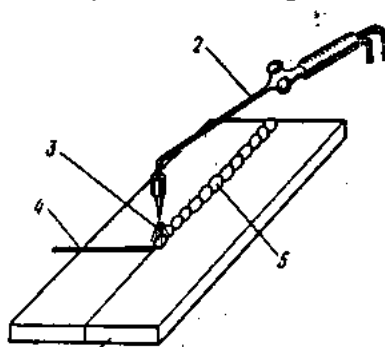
Газовая сварка: 1 – свариваемые детали; 2 – горелка; 3 – пламя сжигаемых газов; 4 – присадочная проволока; 5 – шов.
